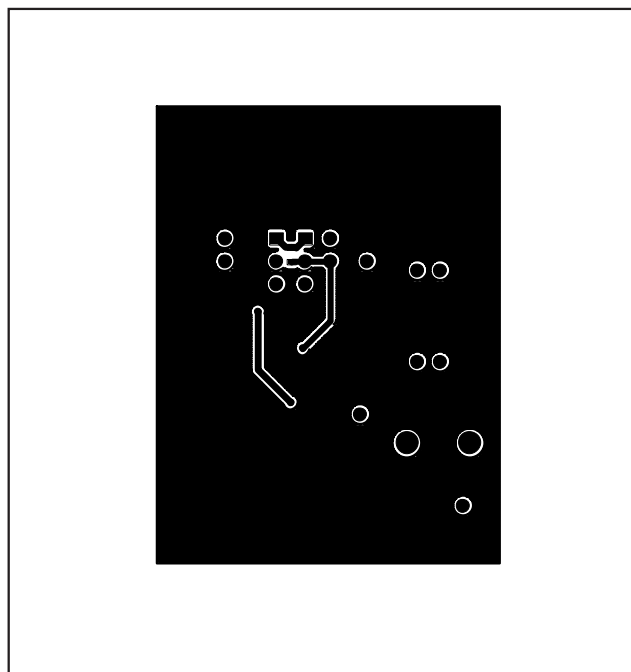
MAX4411 评估板 PC 板布局 — 焊接层
